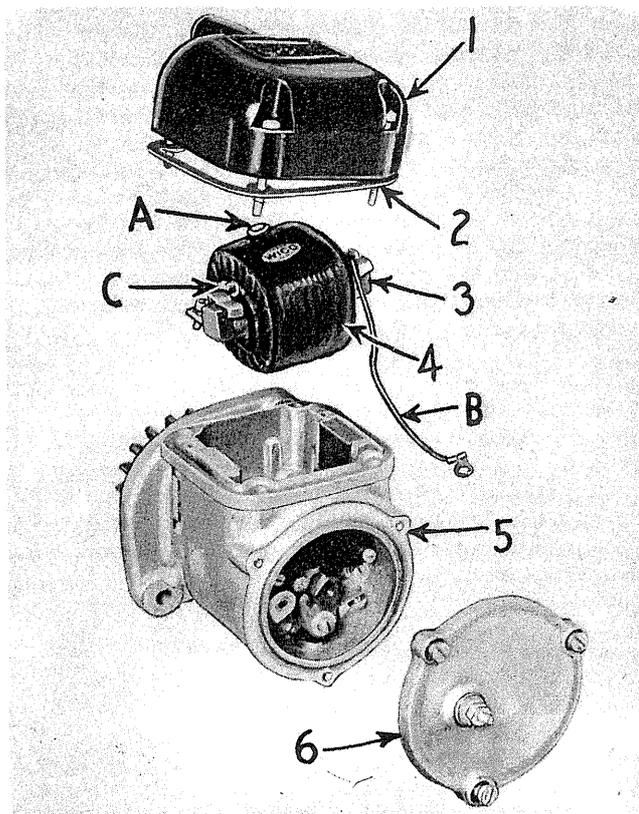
MAGNETO TYPE "AH" DONT ON A ENLEVÉ LA BOBINE. 1 - COUVERCLE DE LA BOBINE. 2 - JOINT DU COUVERCLE. 3 - NOYAU DE LA BOBINE. 4 - BOBINE. 5 - BOÎTIER DE LA MAGNETO AVEC ROTOR RUPTEUR, CONDENSATEUR ET IMPULSEUR. 6 - COUVERCLE DU BOÎTIER DU RUPTEUR.
